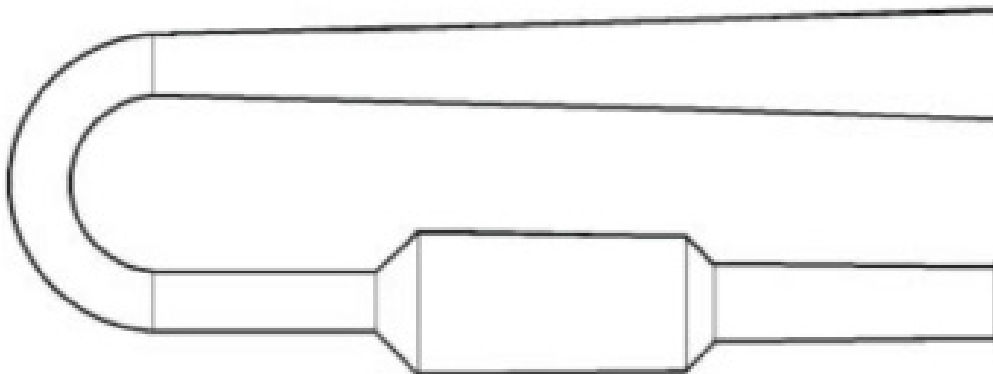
Бесклапанный двигатель конструкции Локвуда-Хиллера
